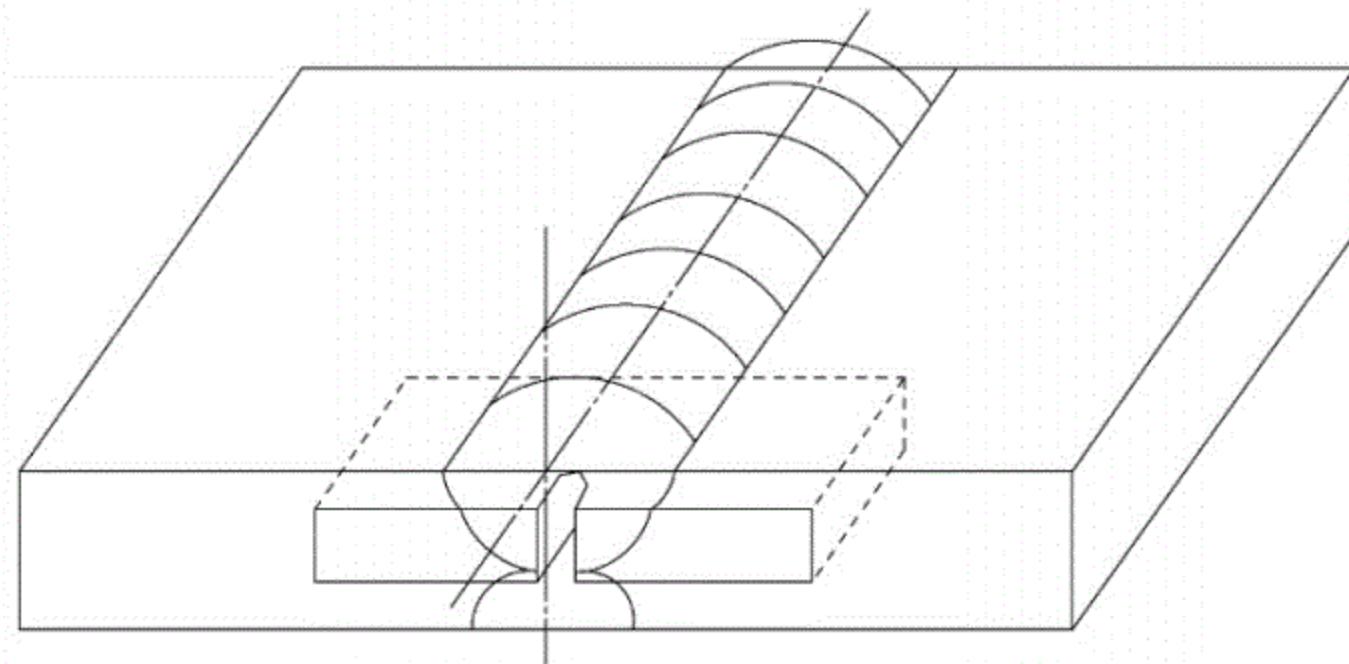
动态撕裂试样焊接接头焊缝金属试样缺口位置示意图
